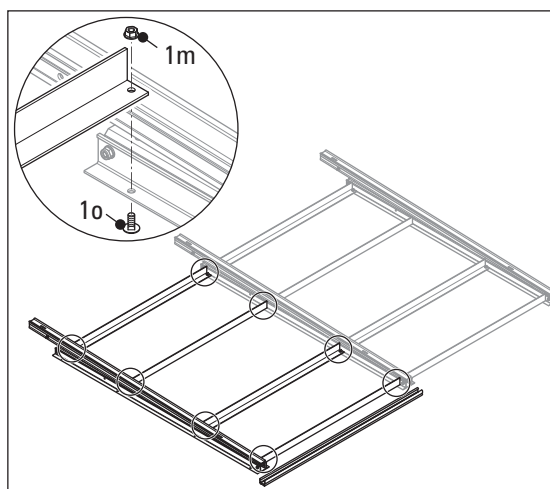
Drittes Grunddreieck mit Querstreben montieren
